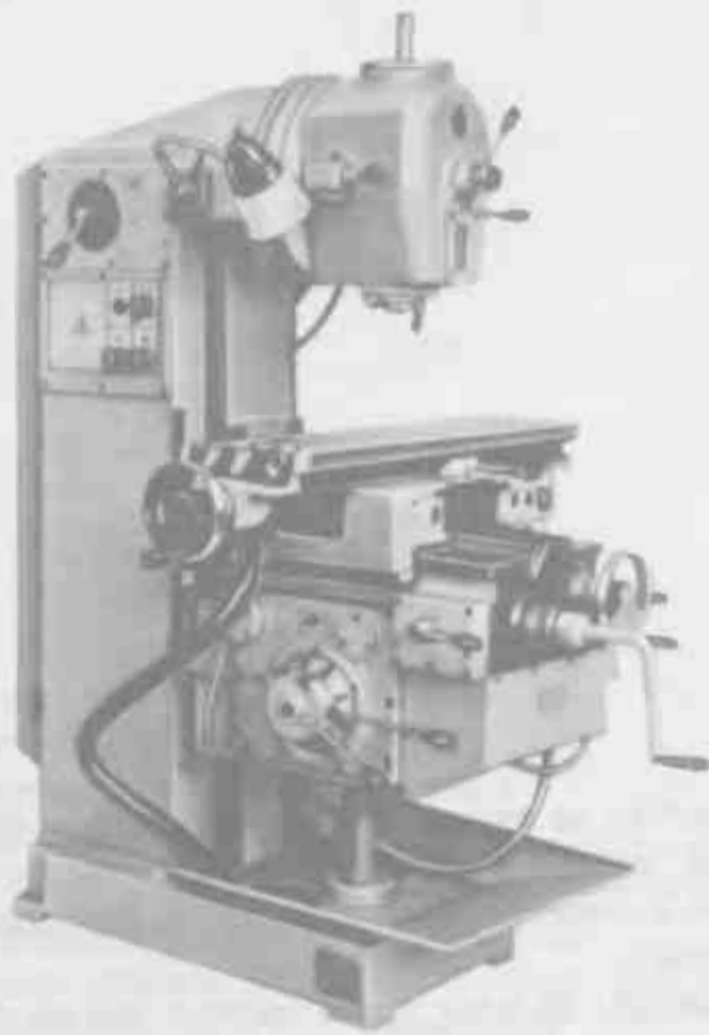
Станок вертикально-фрезерный консольный 6Т10
